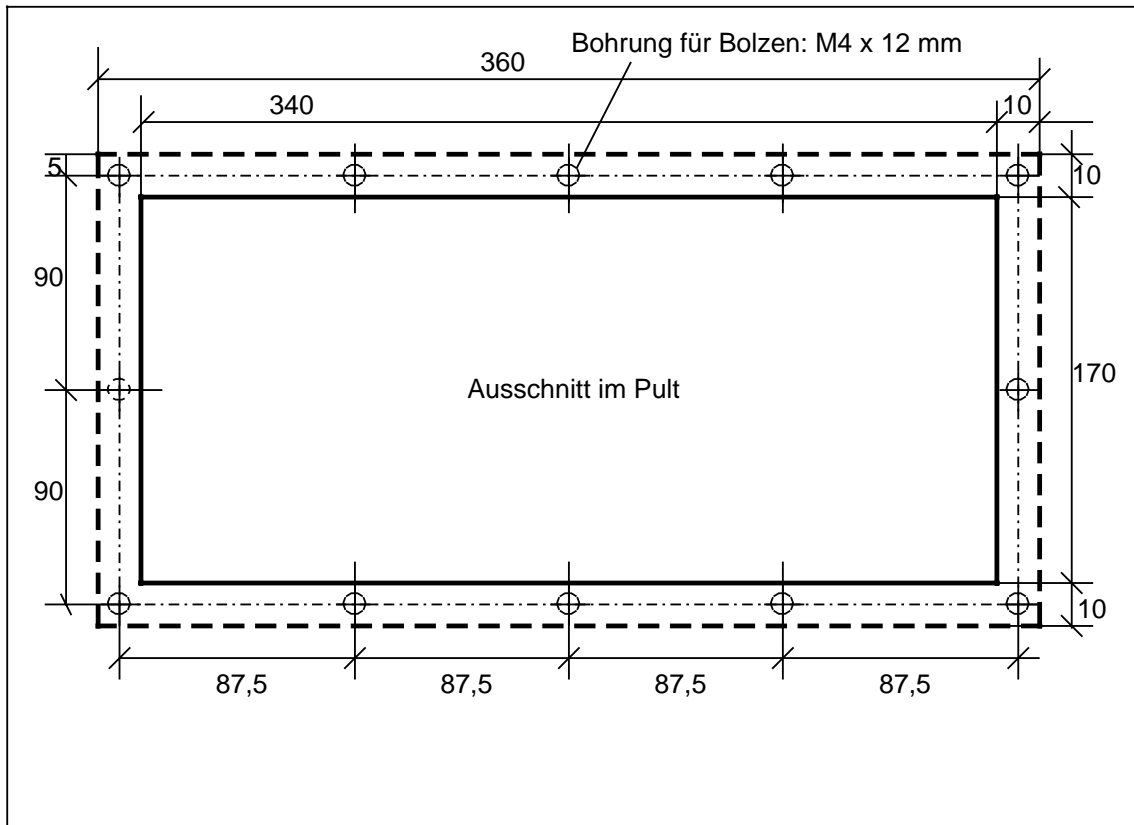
Einbaumaße zum Pulteinbau WS 495/WS 496,
